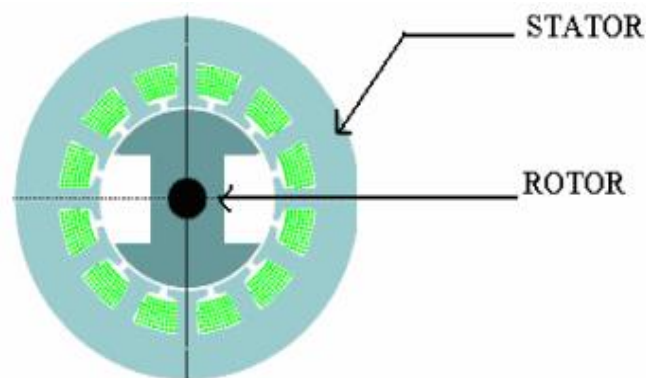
Stator et rotor de la MSRVM. [Ser09]
